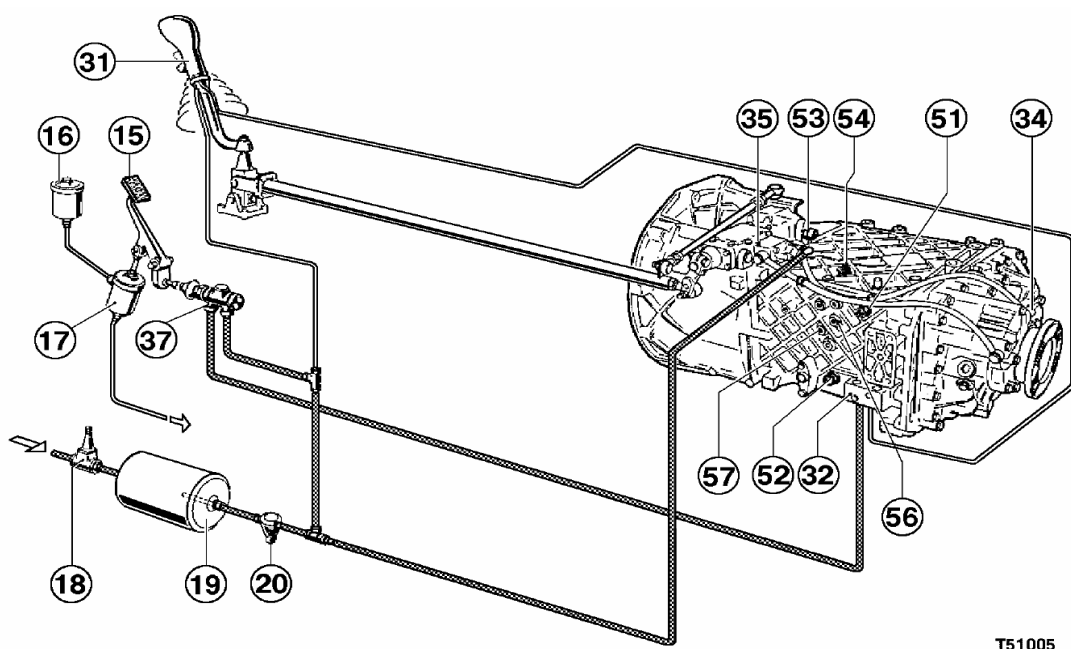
Пневматична система керування коробкою передач ZF-16,
